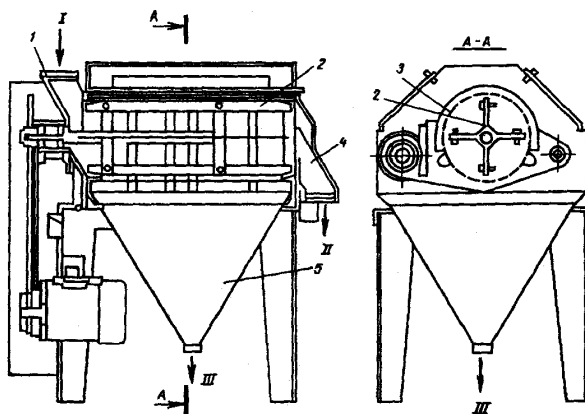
Технологічна схема віброцентрофугала РЗ-БЦА: 1 – прийомний патрубок; 2 – бичевой ротор; 3 – ситовий циліндр; 4, 5 – випускні патрубки; I – вихідний продукт; II – отруб'яністі частки; III – борошніста суміш.
